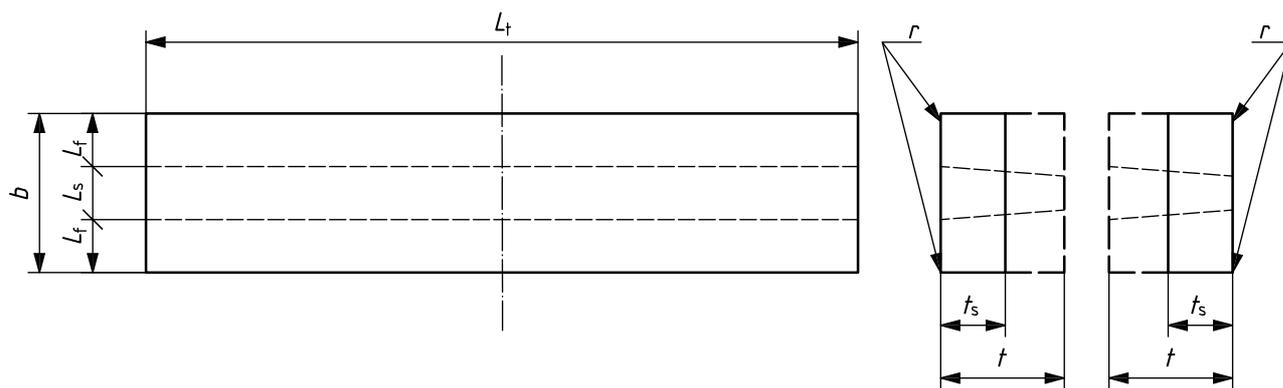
Éprouvette de pliage longitudinal sur soudure bout à bout (LFBB et LRBB)
